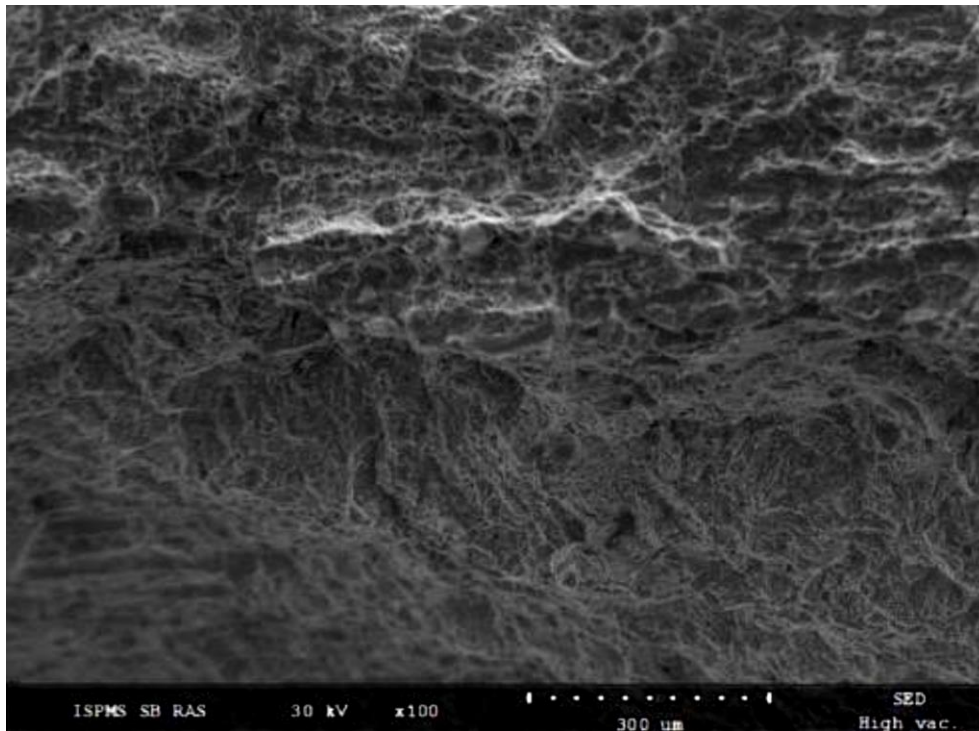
Вигляд поверхні руйнування зварного шва після випробувань
